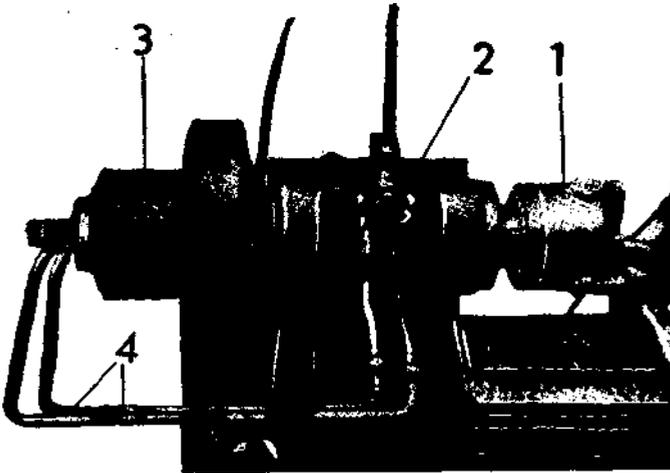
Plato neumático acoplado en un pequeño torno. — 1, Plato. — 2, Válvula de mando. — 3, Cilindro de presión. — 4, Tubos de entrada y salida de aire.
